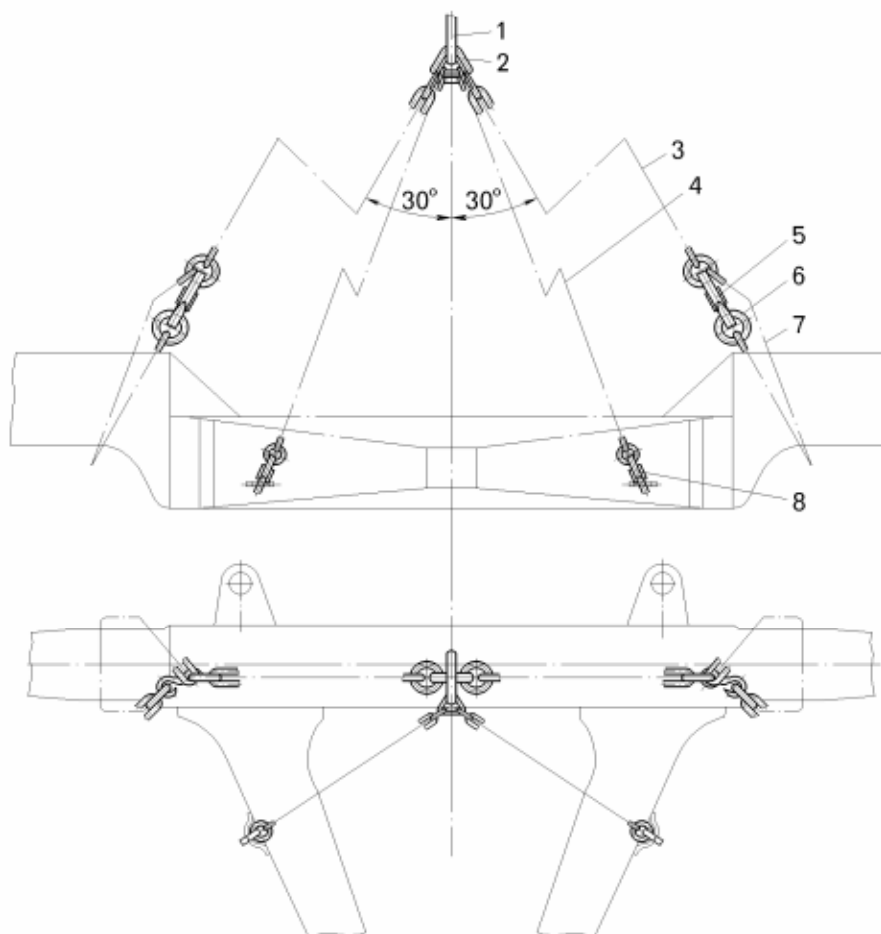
Чалочное приспособление для зачаливания передней оси:
